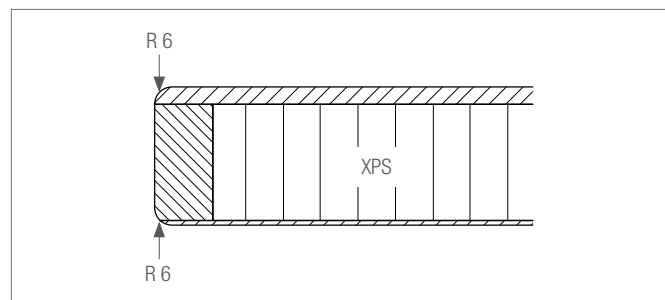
Kanten bündig fräsen und mit Radius versehen
